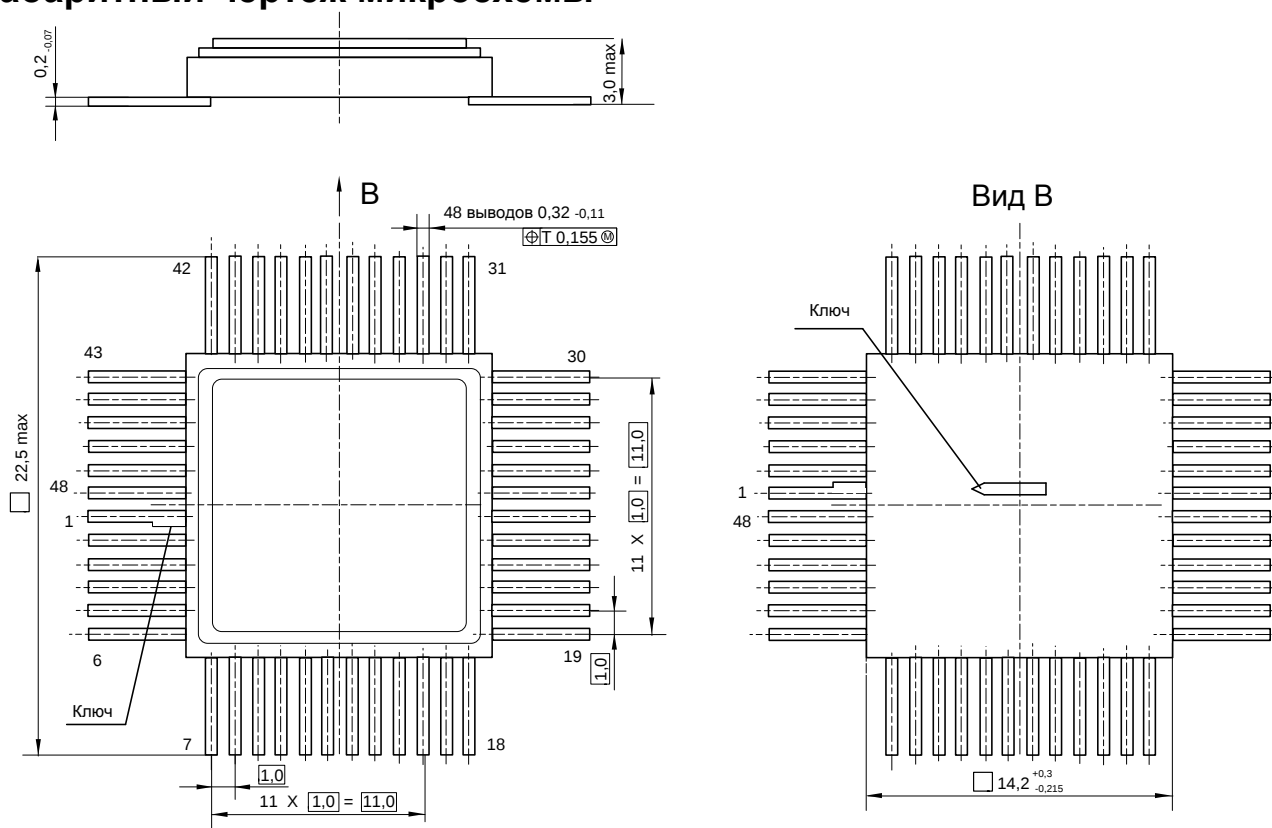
Габаритный чертёж микросхемы в корпусе Н16.48-1В
